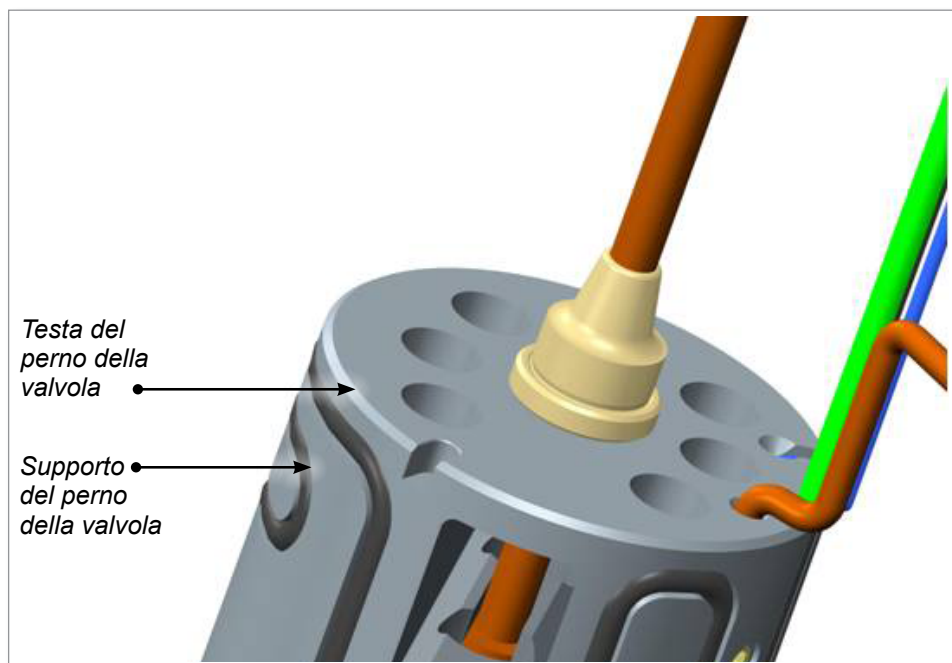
Inserimento del perno della valvola nella scanalatura a buco della serratura
